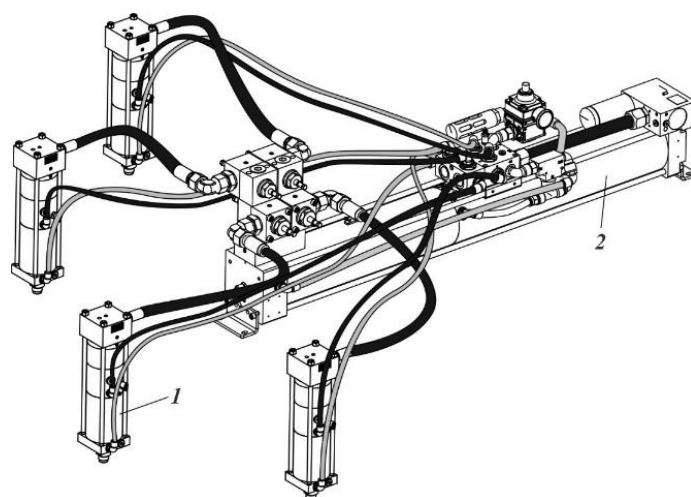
Групповой пневмогидравлический привод TOX Pressotechnik.
